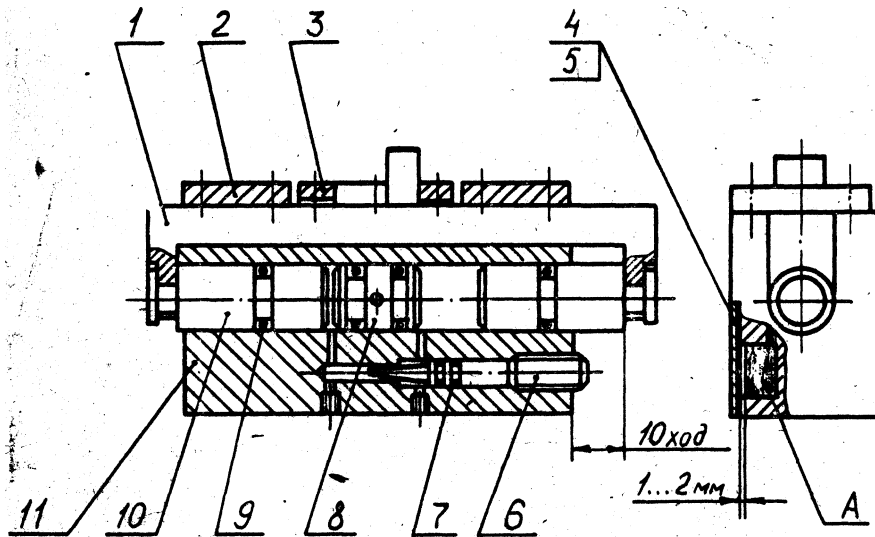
Амортизатор повороту: 1 – скоба; 2 – пластина; 3 – накладка; 4 – кришка; 5 – прокладка; 6 – голка; 7 – кільце гумове; 8 – пробка; 9 – кільце гумове; 10 – шток; 11 – корпус.
